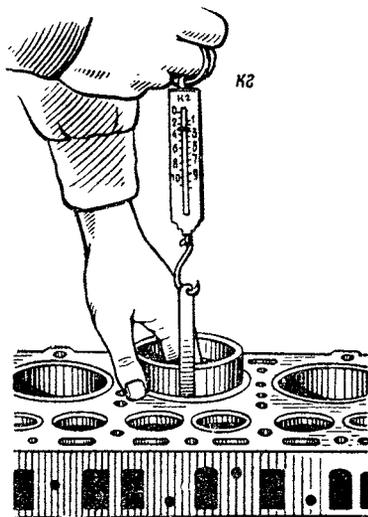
Проверка зазора между юбкой поршня и цилиндром
